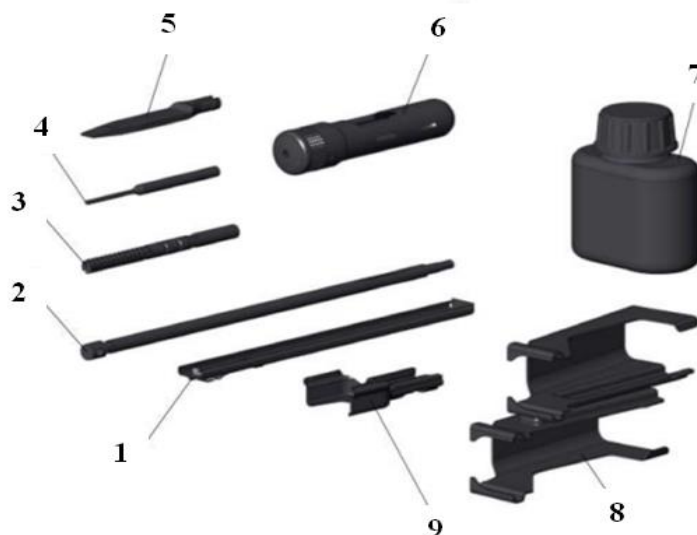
Принадлежность к пистолету-пулемету: 1 – обойма; 2 – шомпол; 3 – протирка; 4 – выколотка; 5 – отвертка; 6 – пенал; 7 – масленка; 8 – крепежное устройство; 9 – переходник
